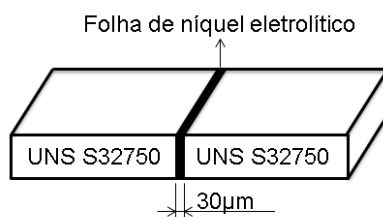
Esquema da junta soldada com a folha de níquel eletrolítico
